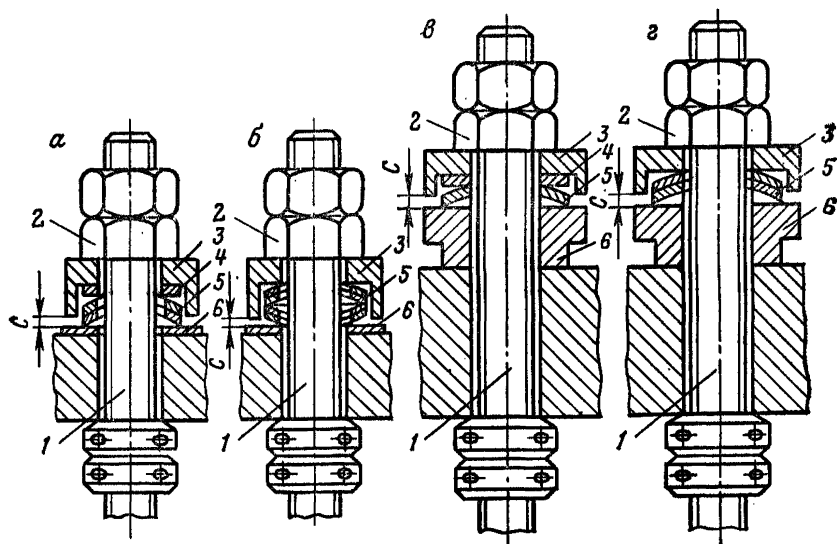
Пружинные звенья исполнительного органа тормоза малых подъемных машин: а—г — типы соответственно 1—4; 1 — тяга; 2 — гайка; 3 — стакан; 4 и б — шайбы; 5 — тарельчатые пружины
